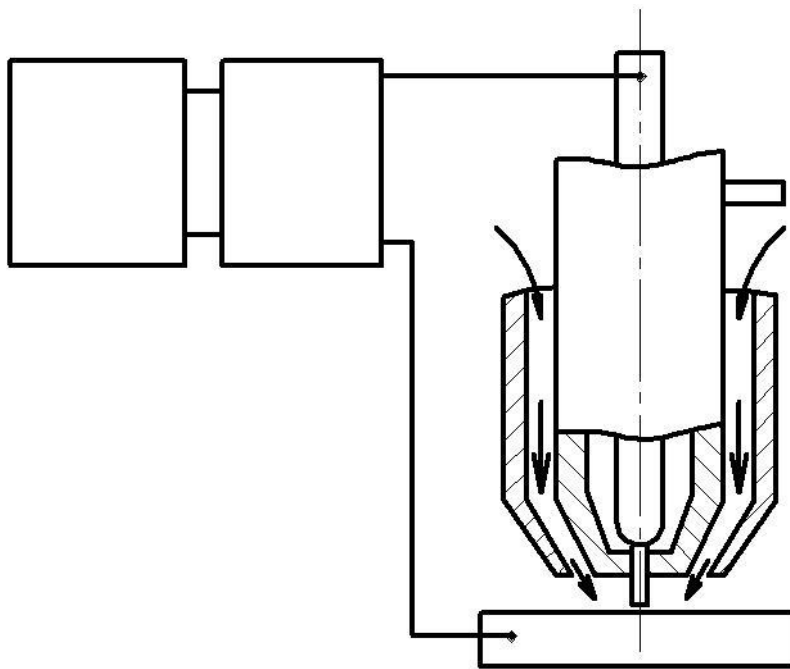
Схема плазменной наплавки с вдуванием порошка в дугу
